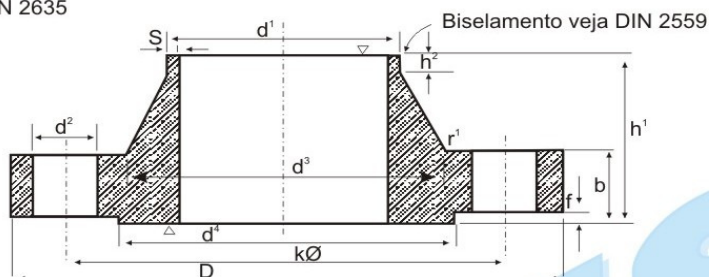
D40 - FLANGE COM PESCOÇO (DIN)
